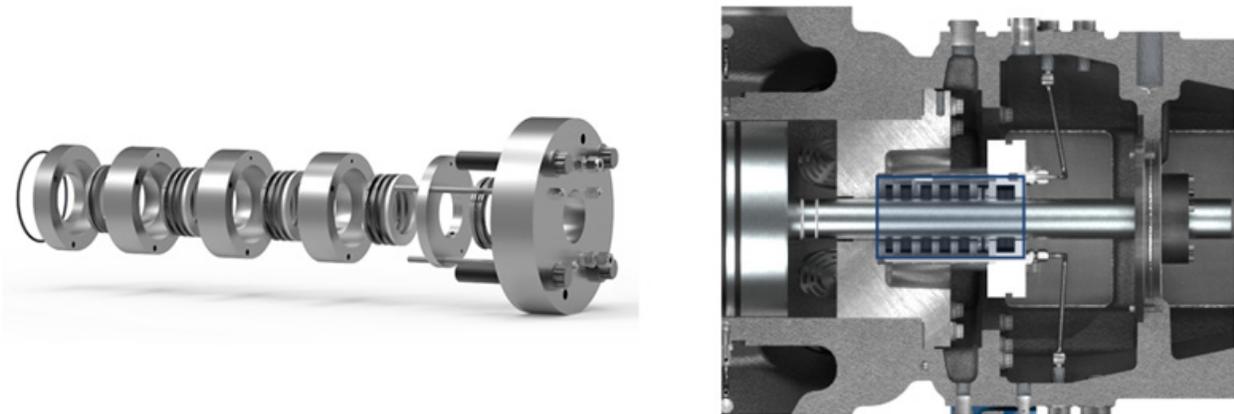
Caja de Empaquetadura - Cilindro Compresor.
